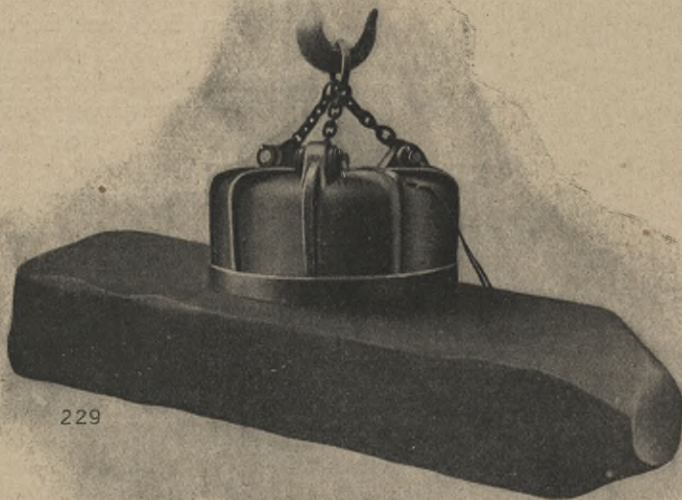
Lastmagnet mit schweren Waßblöcken.
